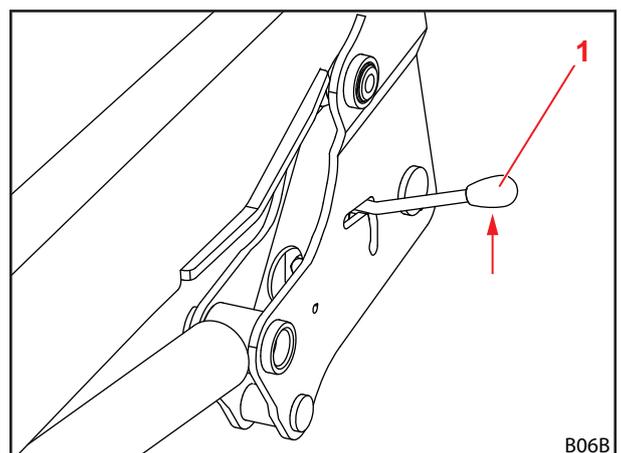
Verificare il dispositivo di bloccaggio del caricatore frontale
